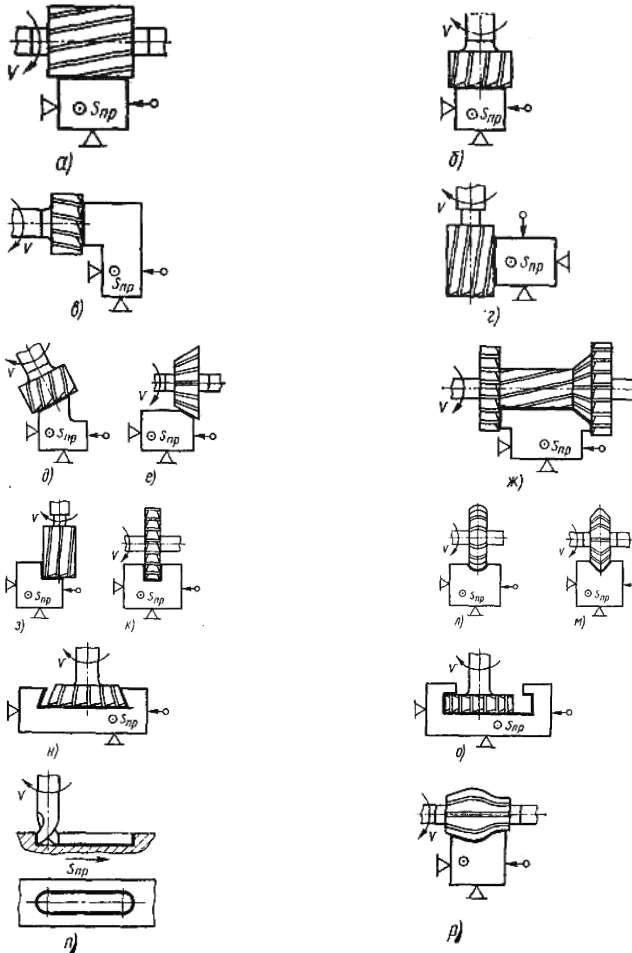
Схеми обробки поверхонь на фрезерних верстатах
